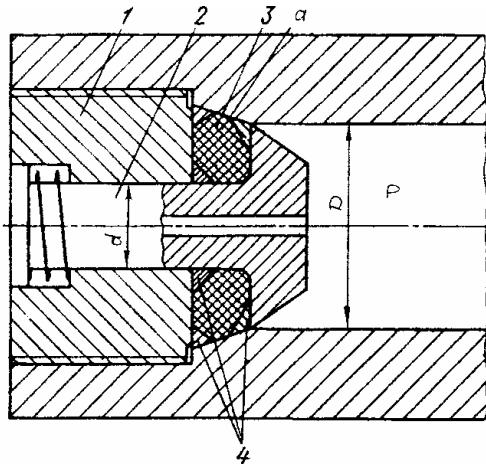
Схема поршневого затвора с упруго-пластическим обтюратором: 1 – затвор; 2 – грибовидный стержень; 3 – обтюрирующая подушка; 4 – кольца; а – обтюрирующий корпус.
